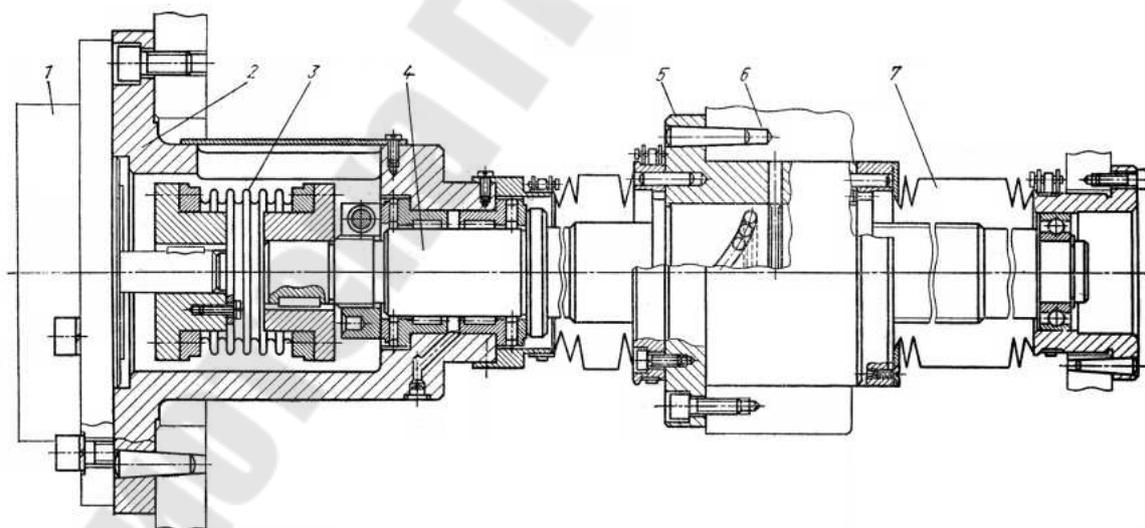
Привод подачи станка с числовым управлением:
